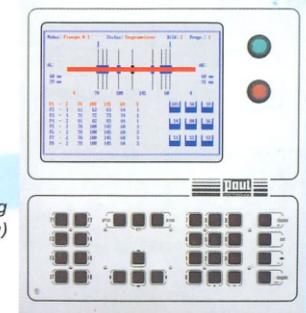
NCD-Steuerung (PC-Schnittbildsteuerung)
